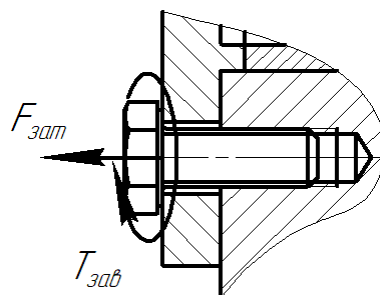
Соединение крышки подшипника с корпусом
